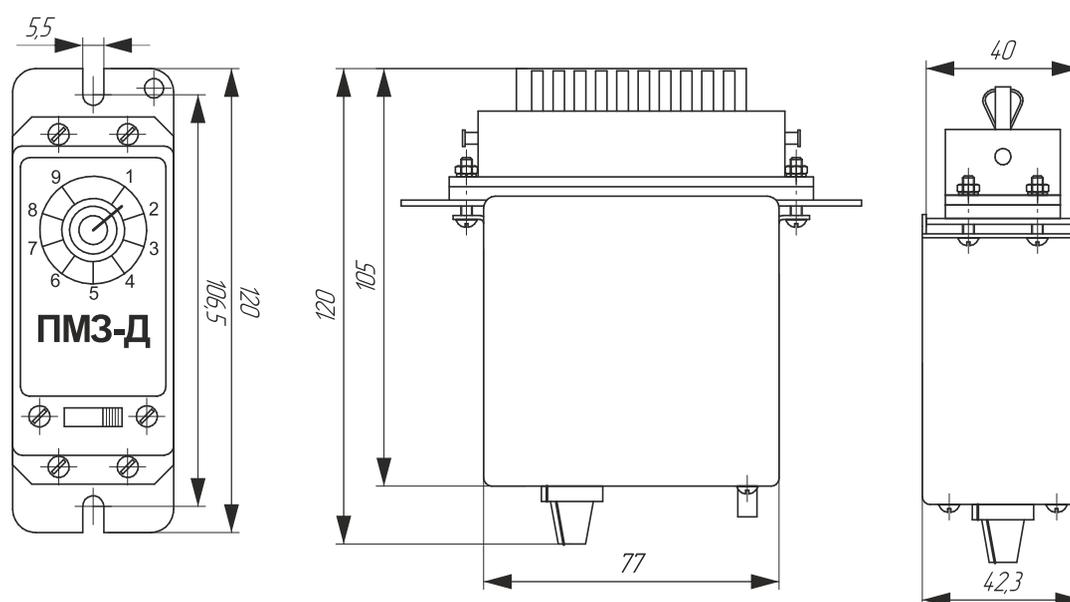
Габаритные и присоединительные размеры блока ПМЗ-Д.
